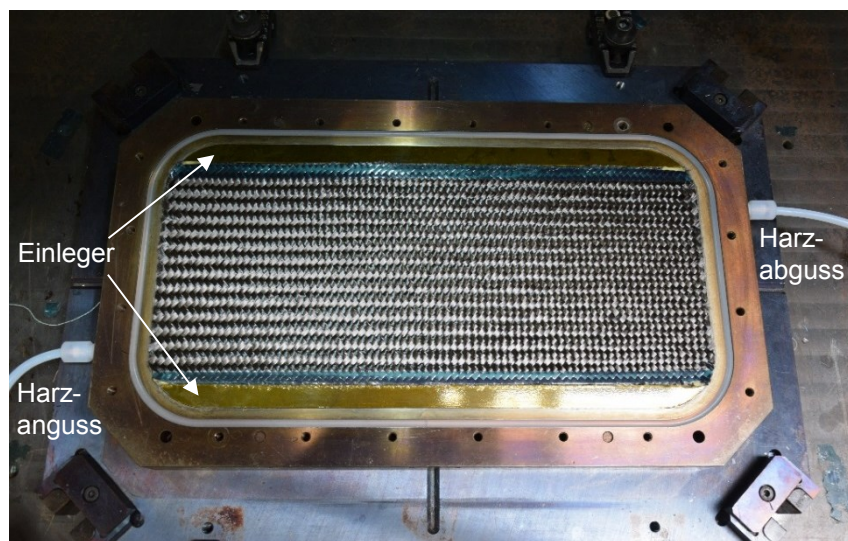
Untere Werkzeughälfte des RTM-Plattenwerkzeugs mit lückenfreier Preform und Einlegern
